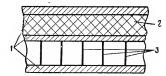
Схема силовой конструкции: 1 — металлические стенки; 2 — легкий заполинтель; 3 — металлические соты
